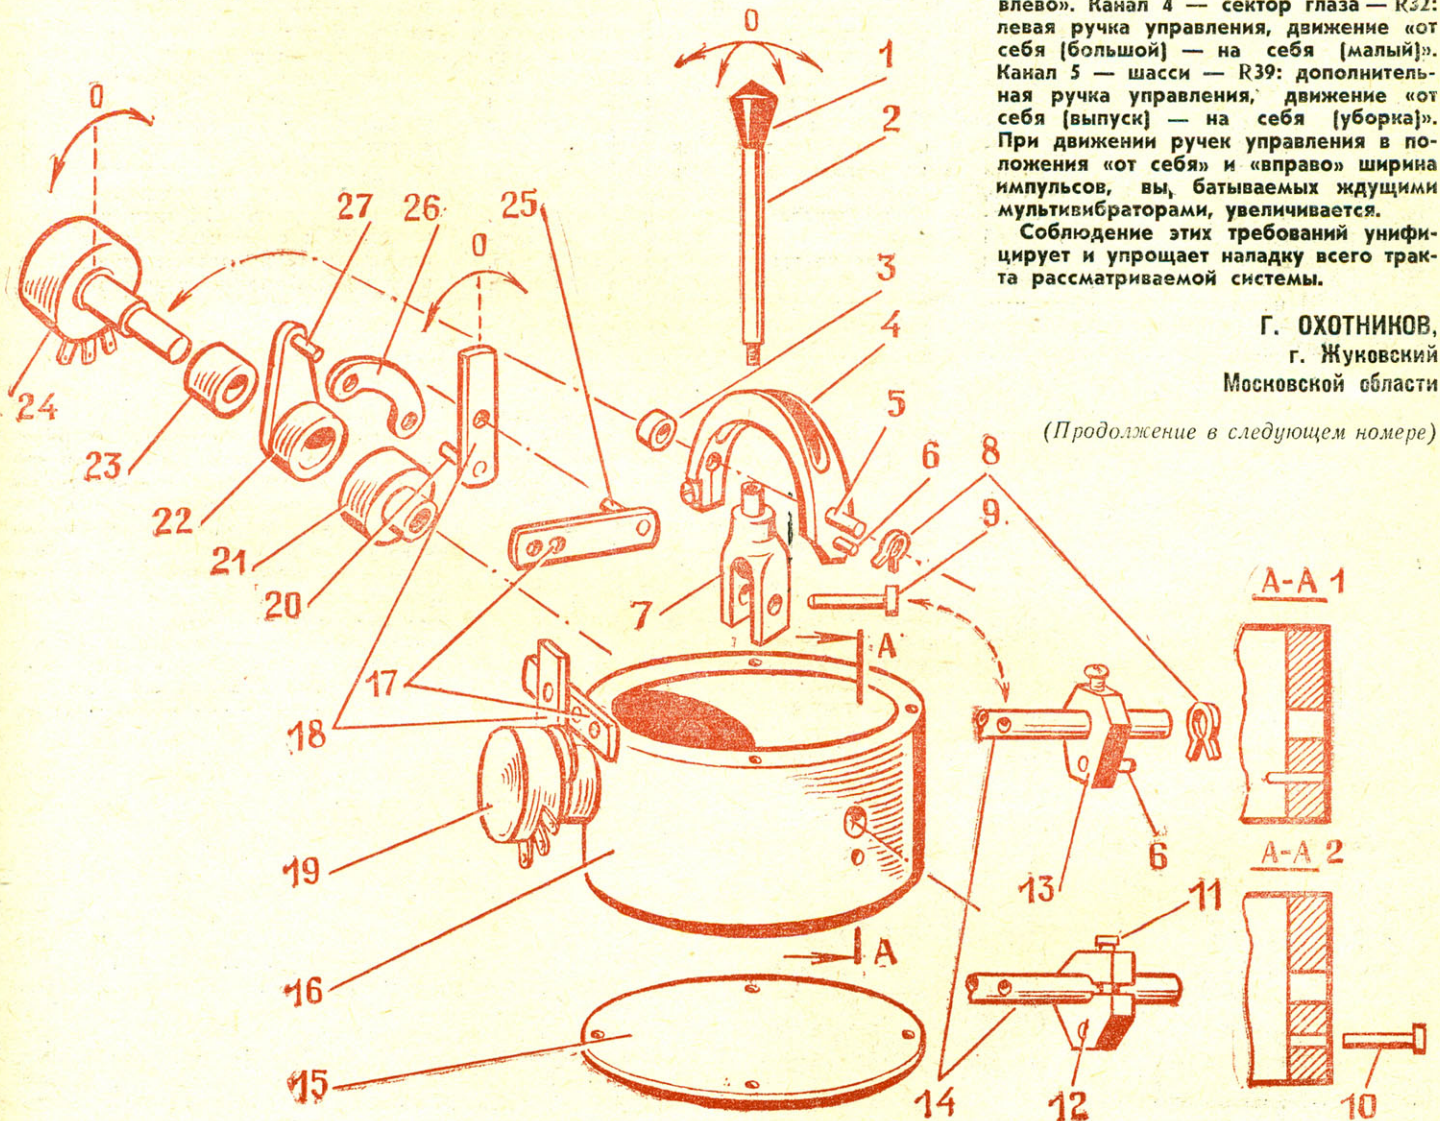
Размещение элементов схемы в корпусе передающего устройства:
